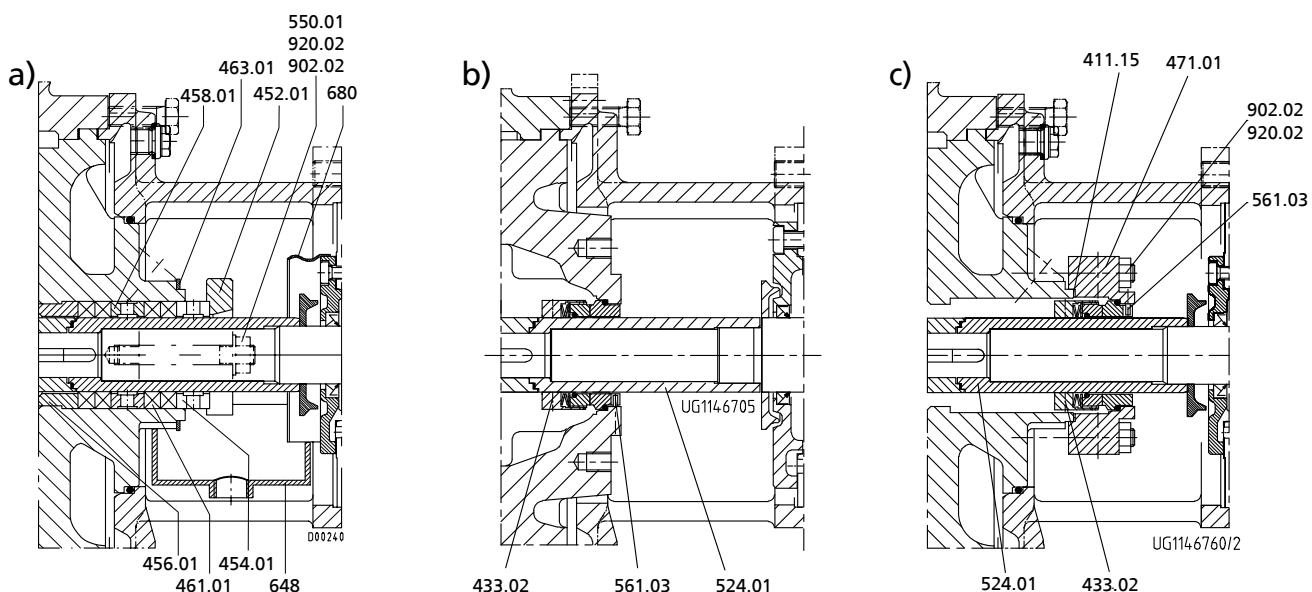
Исполнение с сальниковый набивкой (а), торцевое уплотнение с конической крышкой корпуса (б), торцевое уплотнение с цилиндрической крышкой корпуса (с)
